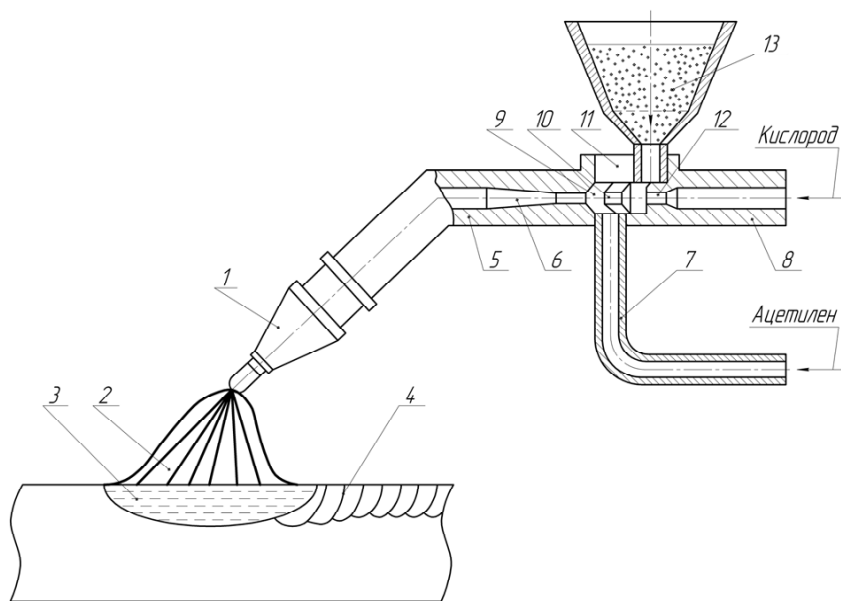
Устройство сварочной горелки: 1 – мундштук; 2 – пламя; 3 – сварочная ванна; 4 – наплавленный слой; 5 – трубка; 6 – канал; 7 – ацетиленовая трубка; 8 – кислородная трубка; 9 – камера смешивания; 10, 12 – инжекторы; 11 – смесительная камера; 13 – порошок
